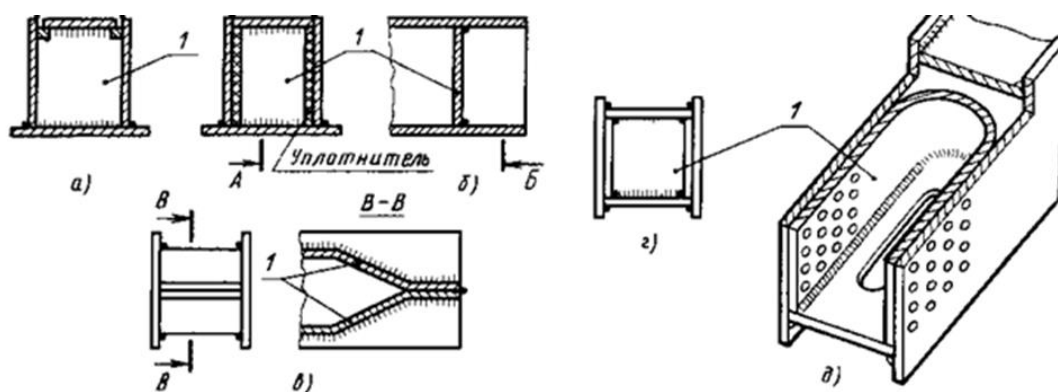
Поперечні перерізи зварних коробчатих балок
